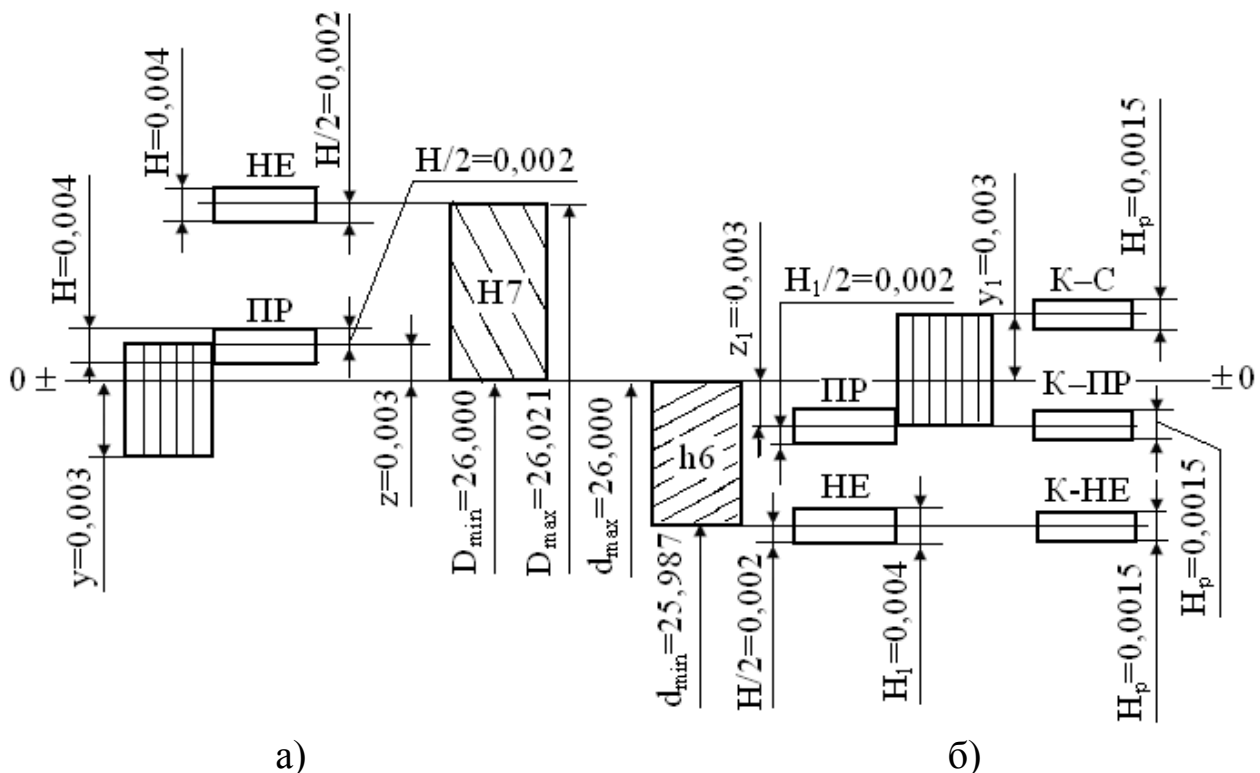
Схеми розташування полів допусків для калібрів:
